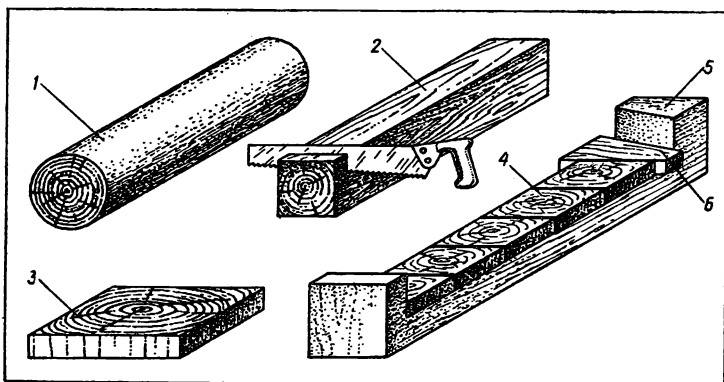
Изготовление клееной торцевой плиты: 1 — заготовка; 2 — брусок; 3 — прямоугольный срез; 4 — набор склеиваемых пластинок; 5 — приспособление; 6 — клин.
